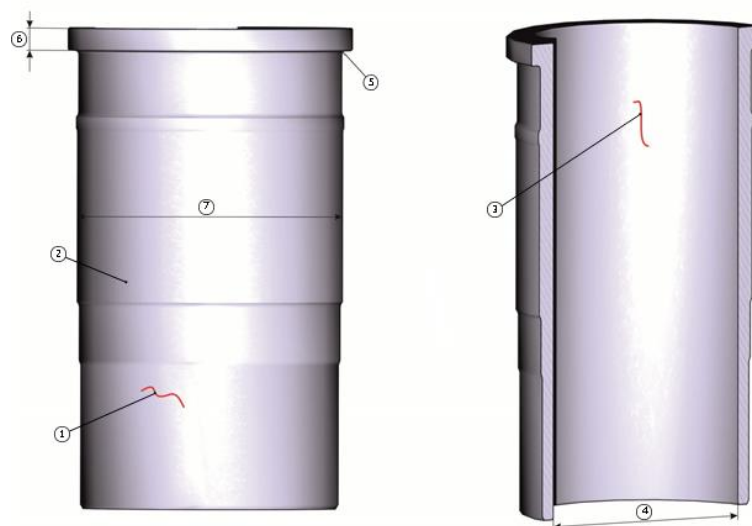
гильза блока цилиндров двигателя ЯМЗ 536
